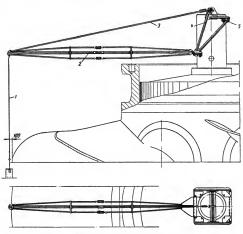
Схема проверки концентричности лопастей рабочего колеса. I- струна с отвесом; 2- стрела; 3- трос; 4- рама; 5- ролики.
